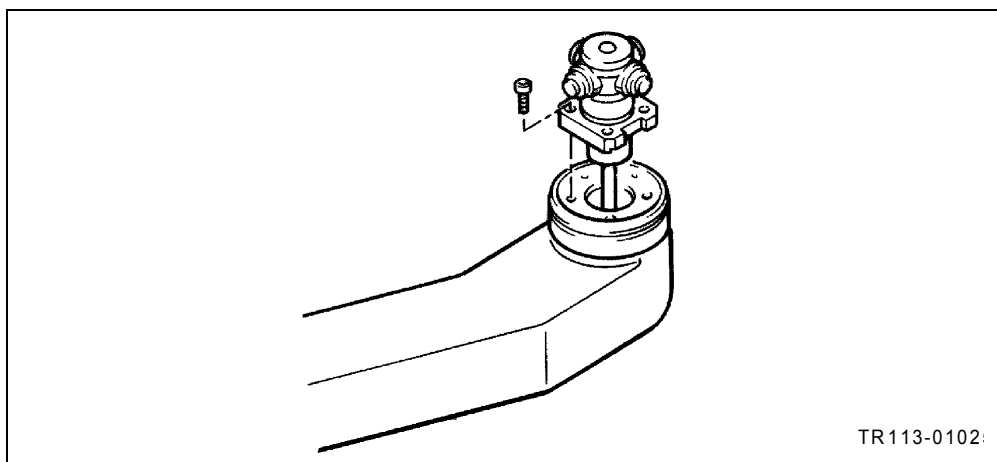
Замена датчика TOOL EYE (4/4)
